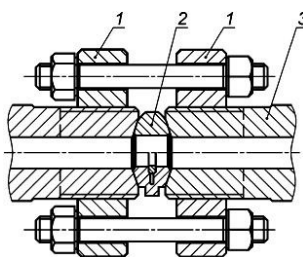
Фланцевое РС с резьбовыми фланцами
